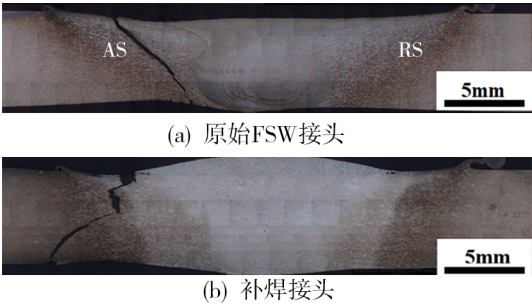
原始 FSW 接头及补焊接头横截面断裂路径
